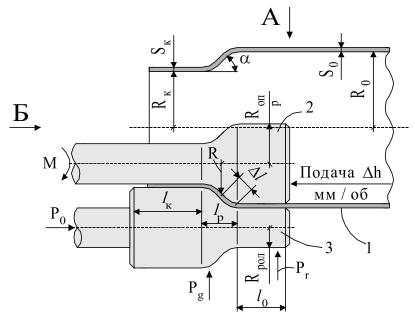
Схема ротационного обжима труб: 1 – заготовка; 2 – оправка; 3 – ролик
